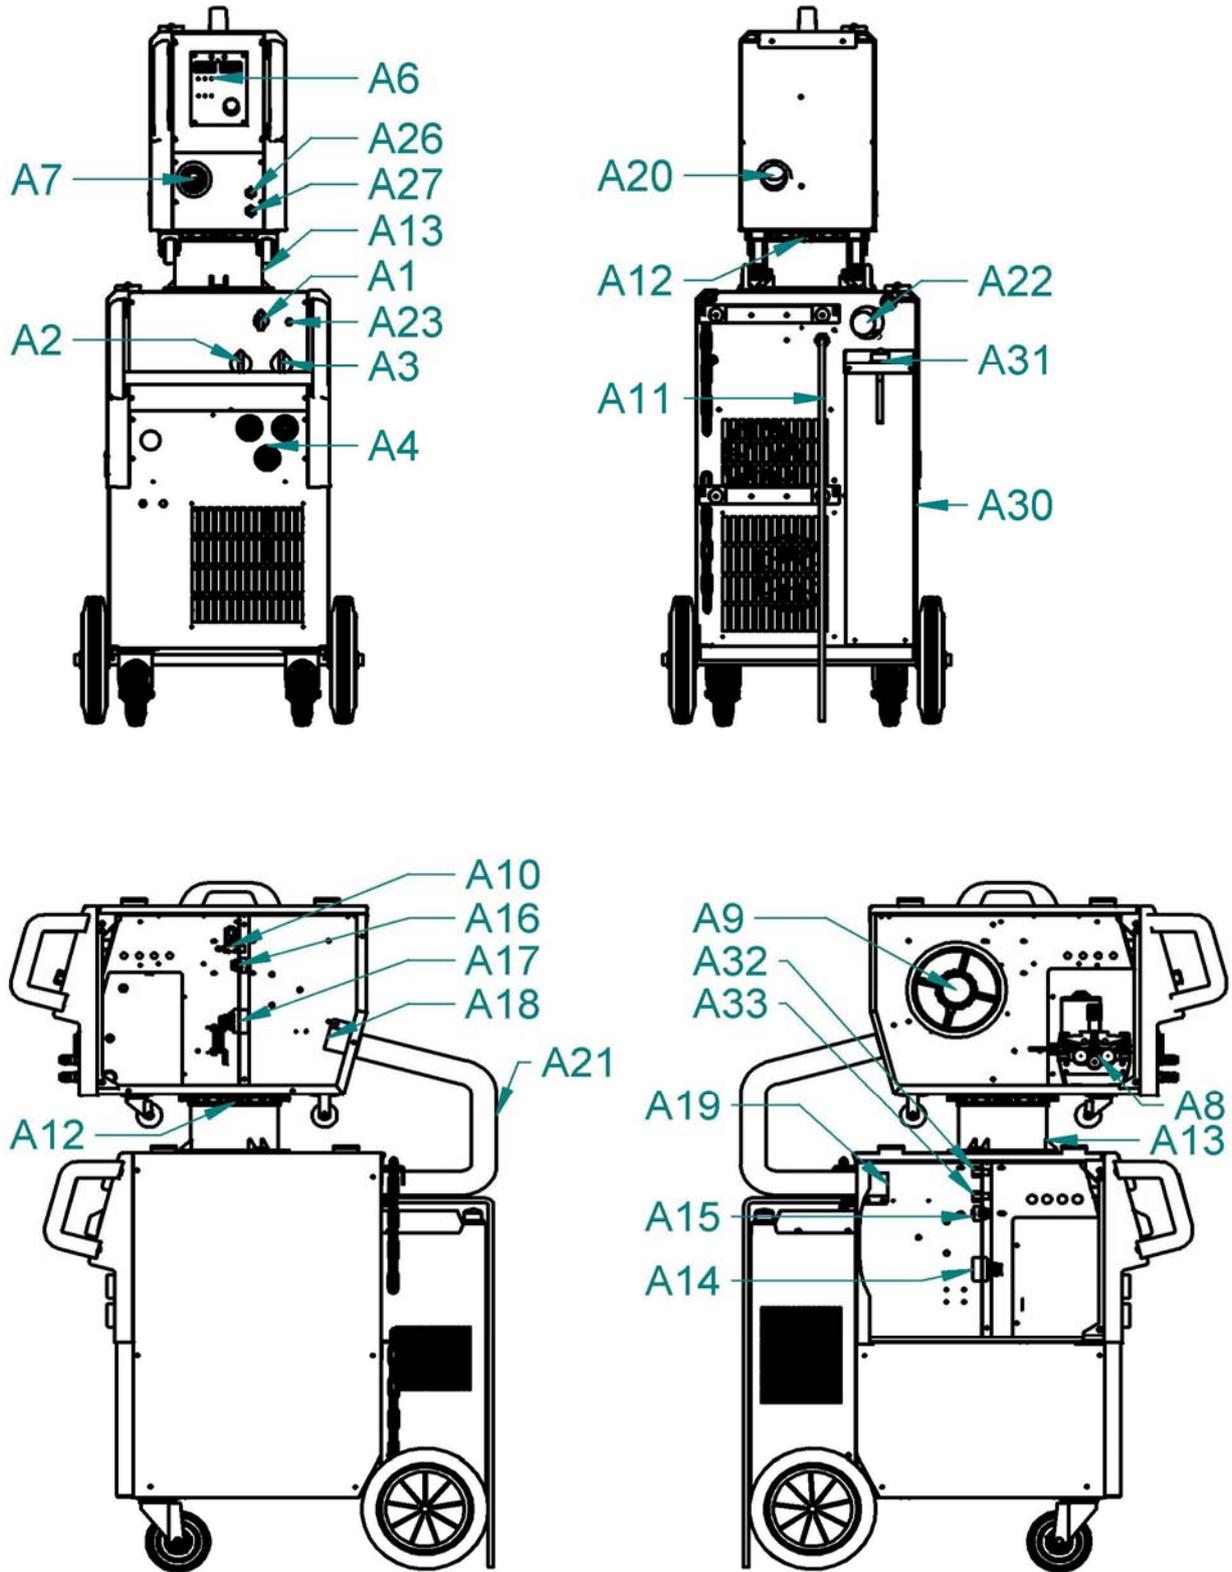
Hauptteile der Maschine Ryval 400-500 aXe
